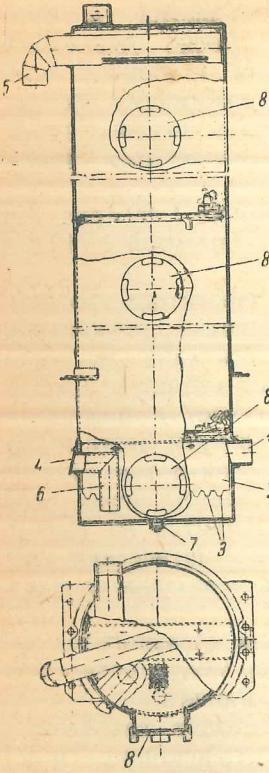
Тонкий очиститель газогенераторной установки Г-69:
